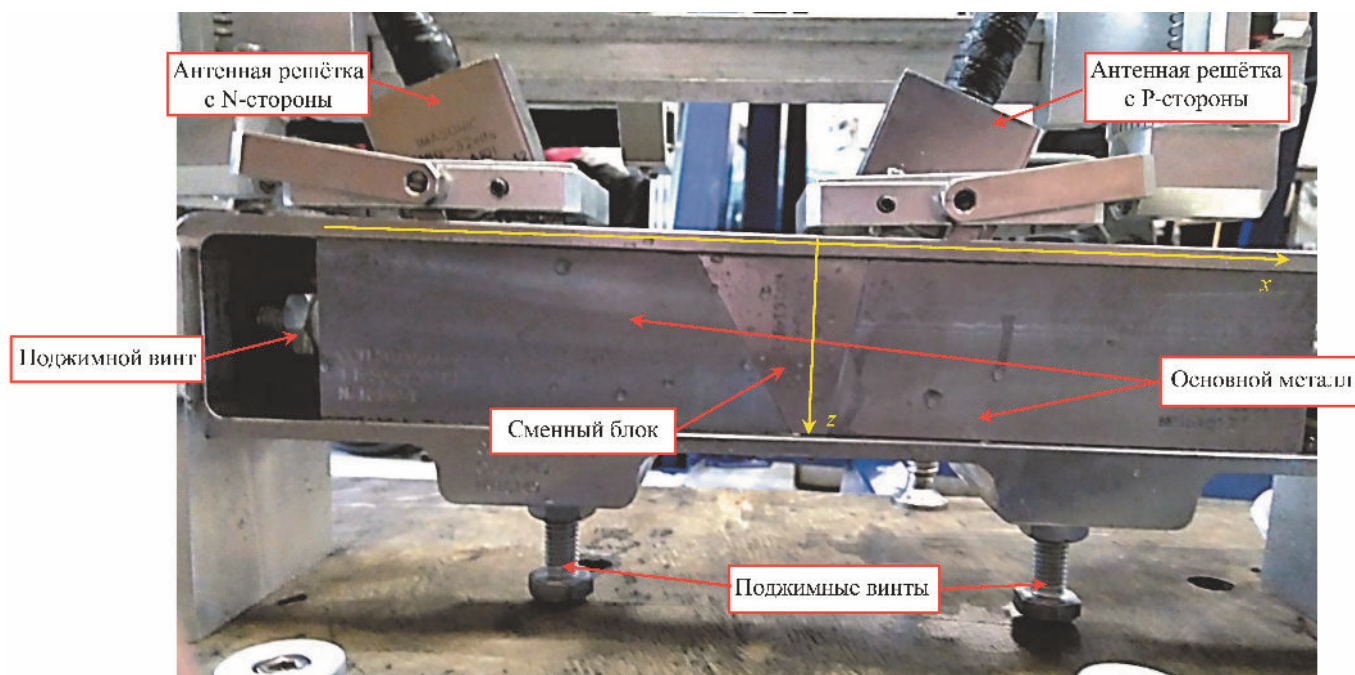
Стенд со сменным блоком из аустенитной стали, имитирующий сварное соединение
